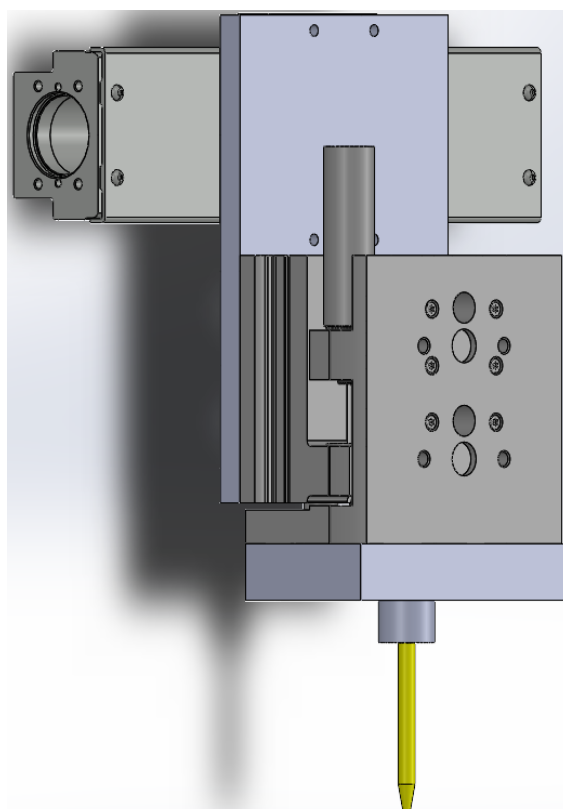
Верхний сварочный контура с возможностью линейного перемещения
